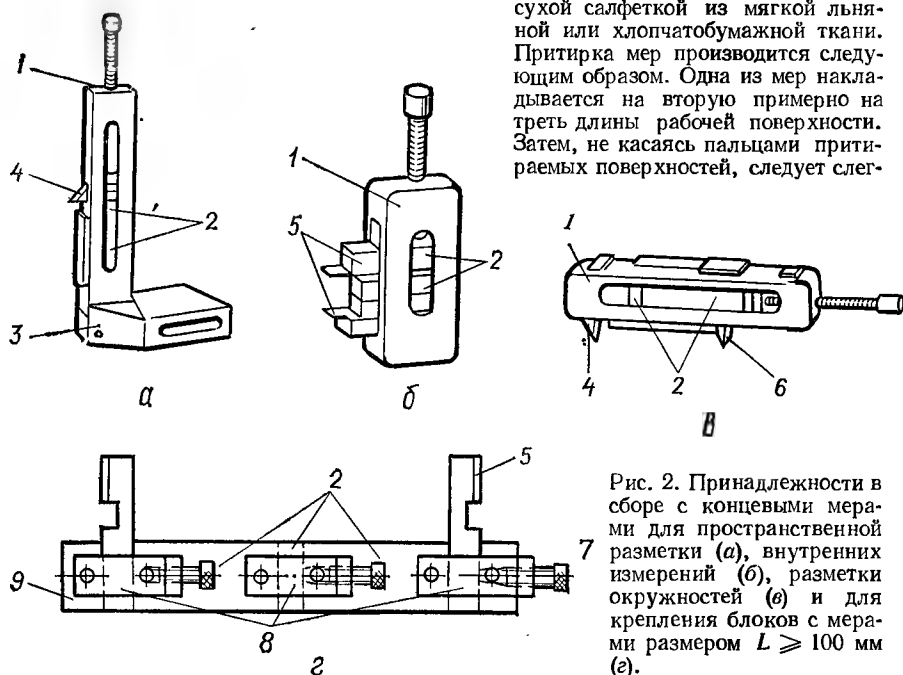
Принадлежности в сборе с концевыми мерами для пространственной разметки (а), внутренних измерений (б), разметки окружностей (в) и для крепления блоков с мерами размером $L \geq 100$ мм (г).
